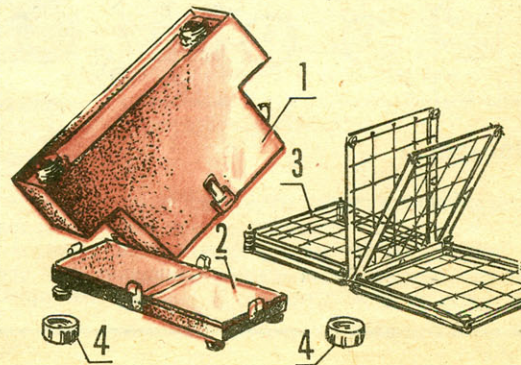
Элементы фотобачка для бумаги: 1 — корпус, 2 — дно, 3 — кассета, 4 — навинчивающиеся пробки горловин.
